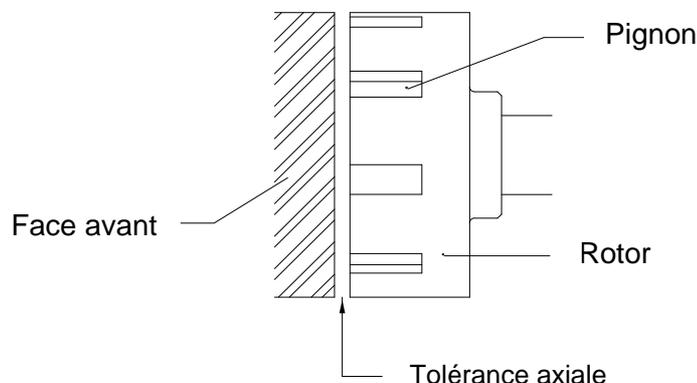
montre les tolérances axiales entre le rotor et la face avant.
